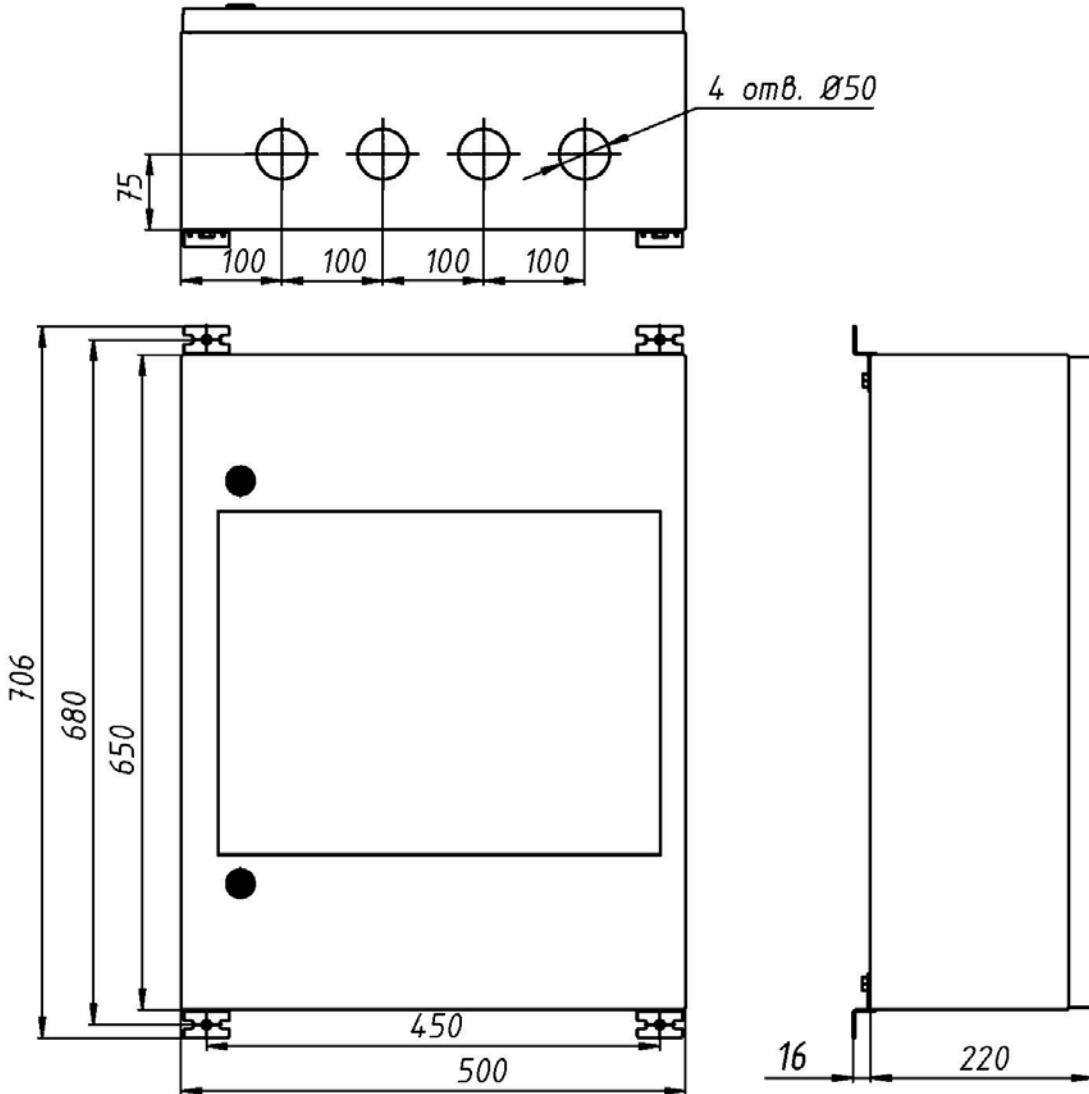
Габаритные размеры корпуса ППО КСПИ Эгида
